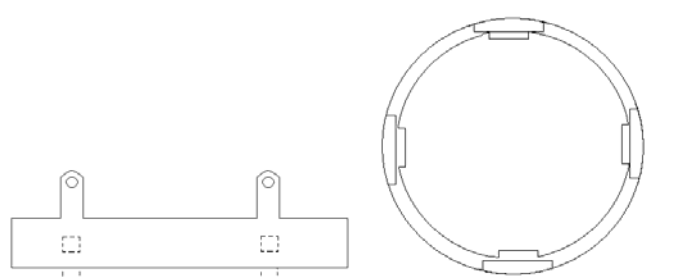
Interfaz Sistema de Suspensión-Socket del lado de la malla. Izquierda vista frontal, derecha vista superior
